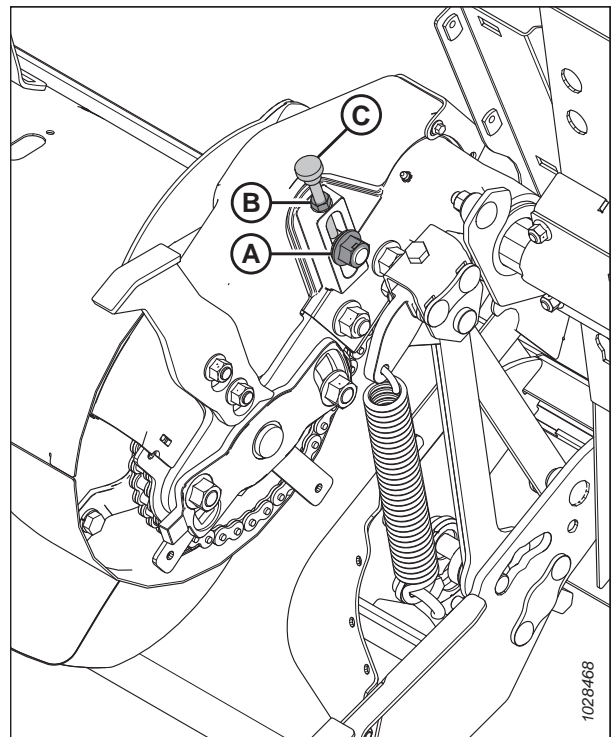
Левая сторона привода шнека - вид спереди
